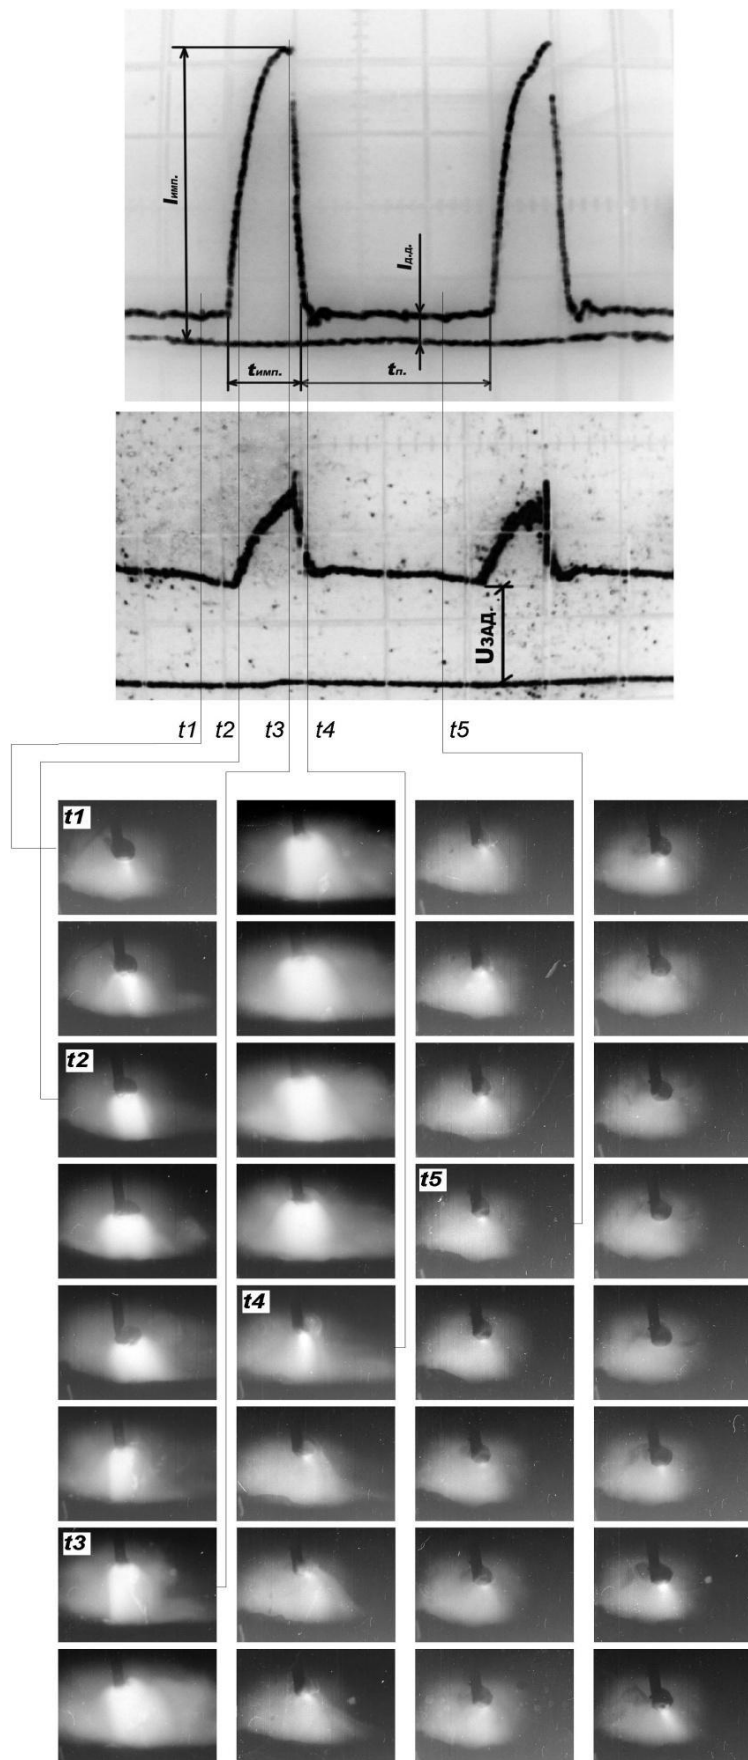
Совмещённые осциллограммы сварки и кинокадры процесса при сварке с использованием импульсной дуги [3]
